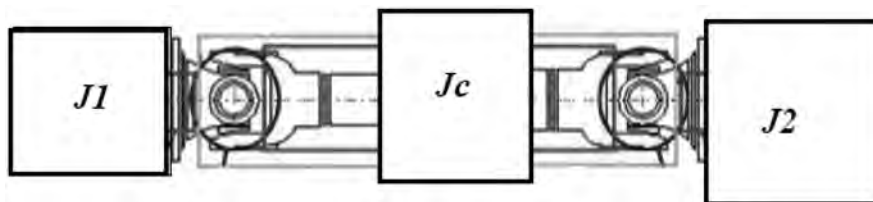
Модель главного привода рабочих валков прошивного стана ТПА со шпинделями типа «Карданный вал» (на примере Cardan Shaft)
